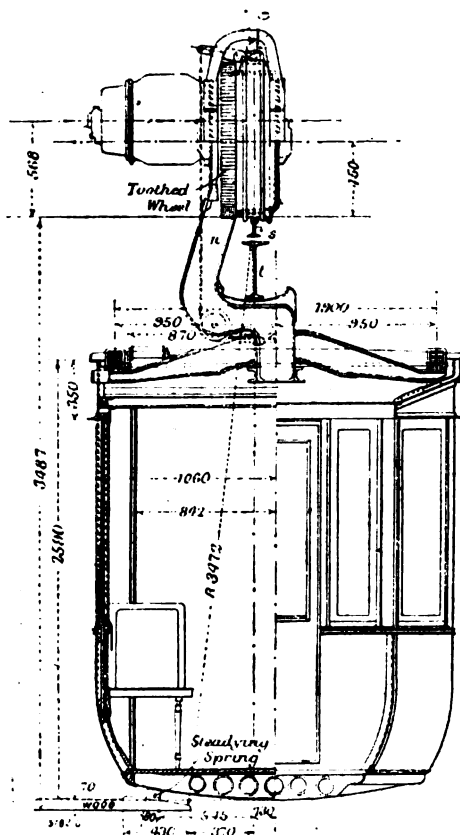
Coupe des voitures du monorail suspendu de Barmen à Elberfeld.
